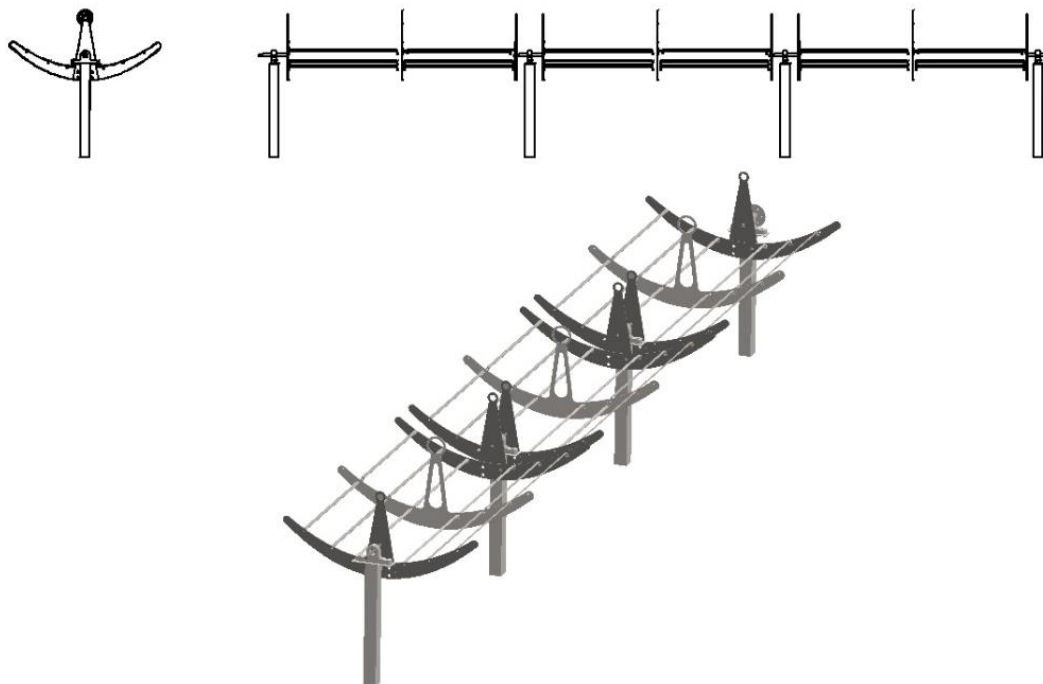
Mise en plan du collecteur micro cylindro parabolique
